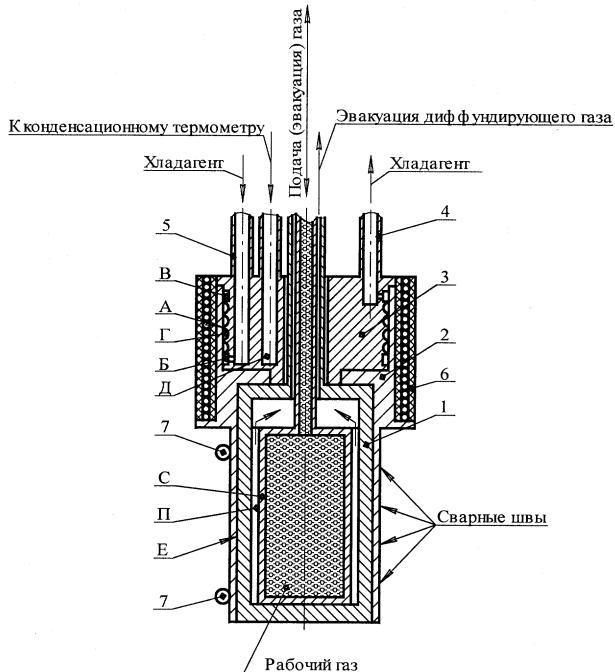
Схематическое изображение мишенного блока: 1 – ампула; 2 – корпус; 3 – вкладыш; 4,5 – штуцеры; 6 – нагреватель; 7 - термопары
